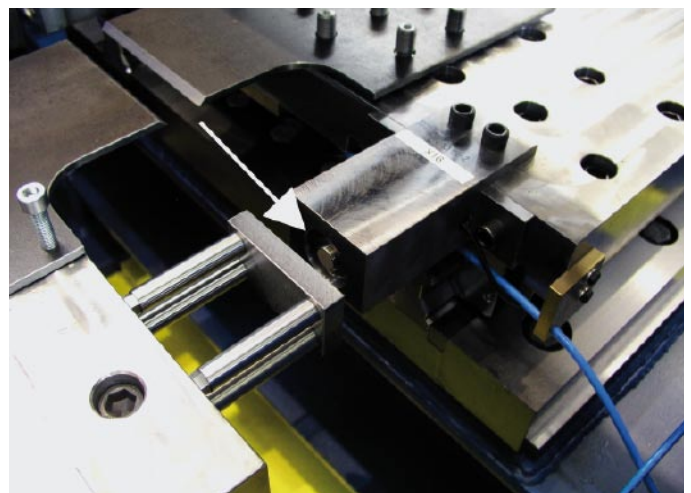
Wirbelstromsensoren eddyNCDT erfassen die Nahtflankenbewegung auf zwei Achsen beim Schweißprüfstand.
